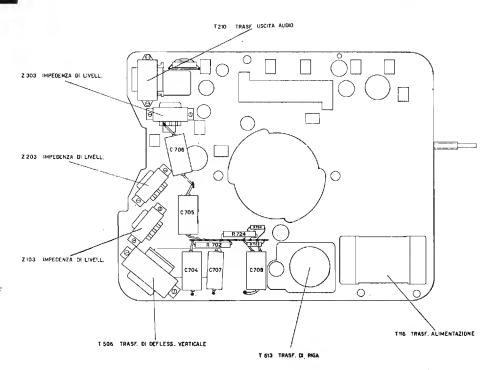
Disposizione dei componenti sulla parte inferiore dllo chassis del televisore CM901.
